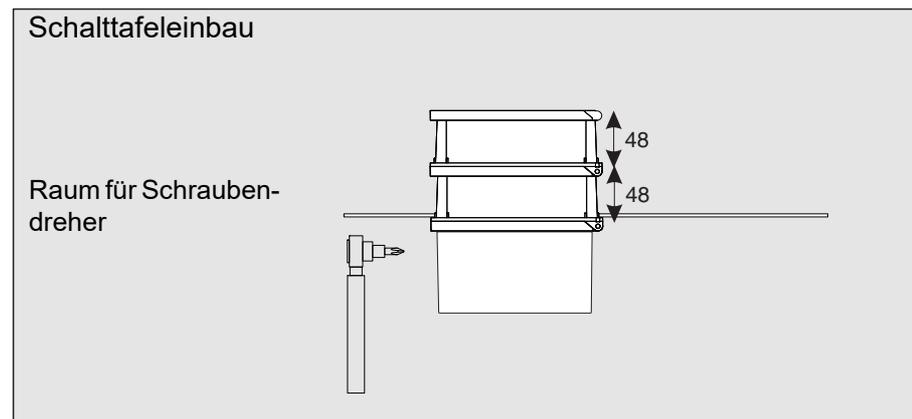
Raumbedarf für Schalttafeleinbau (PMS/IQ) (Maße in mm)
